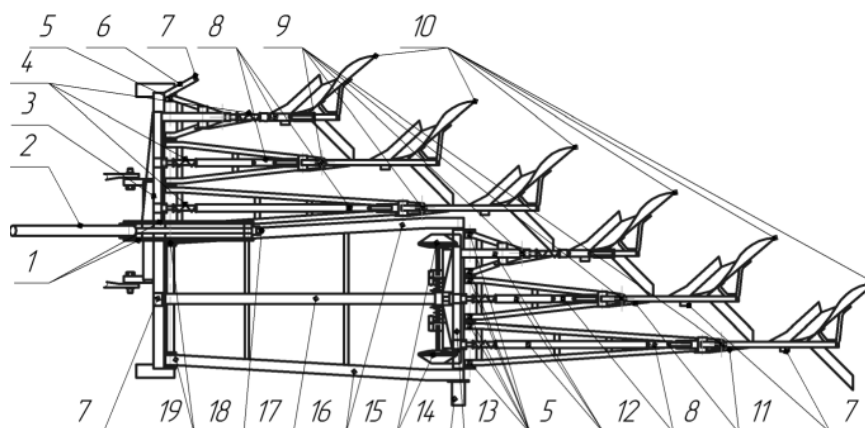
Плуг шестикорпусный, вид сверху:
